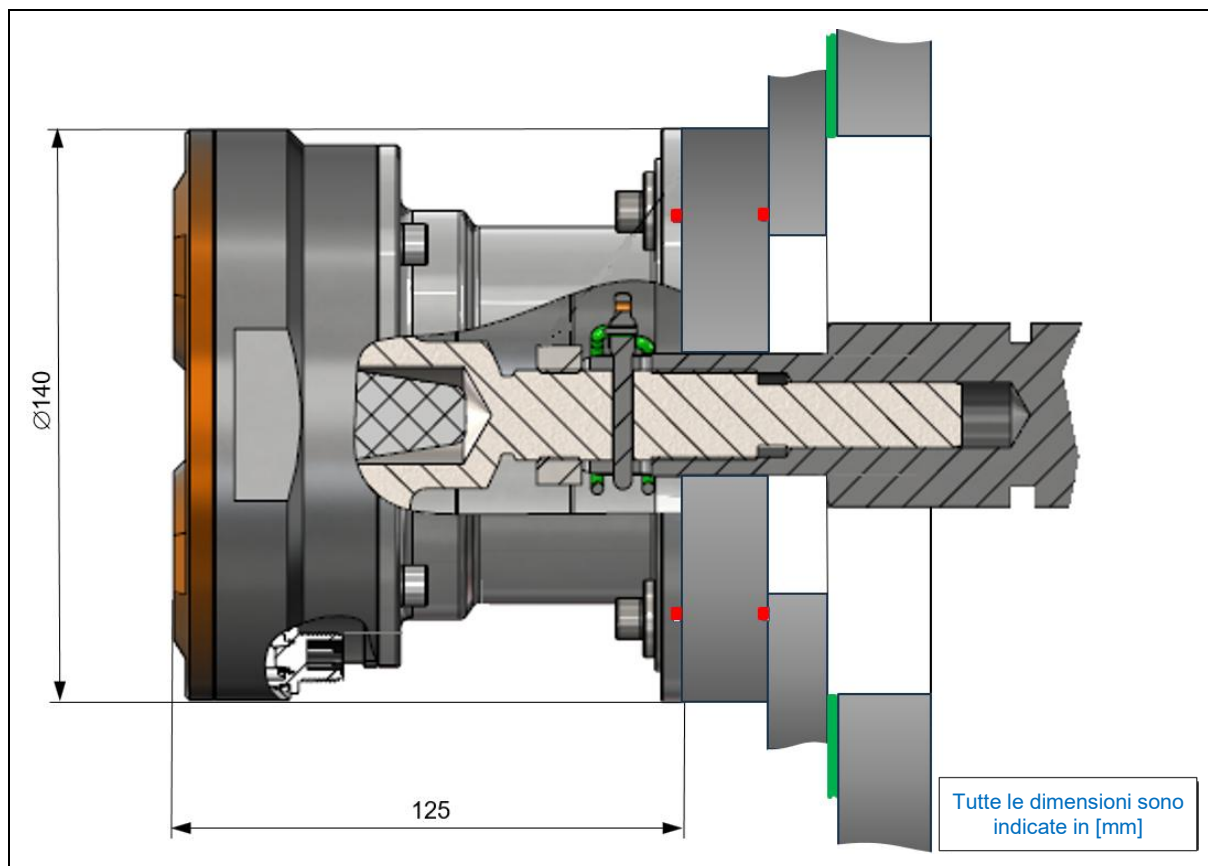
BEAROMOS® 2020 con sistema di tenuta per albero motore montato
